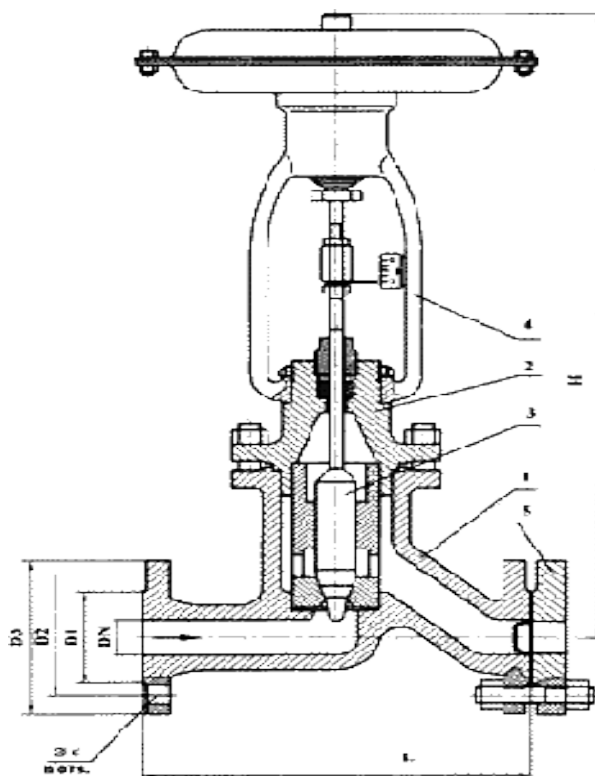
Клапан 25ч42нж: 1- корпус; 2- кришка; 3- плунжер;
